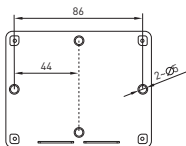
Отверстия для крепежа на стену ТНТ-101
